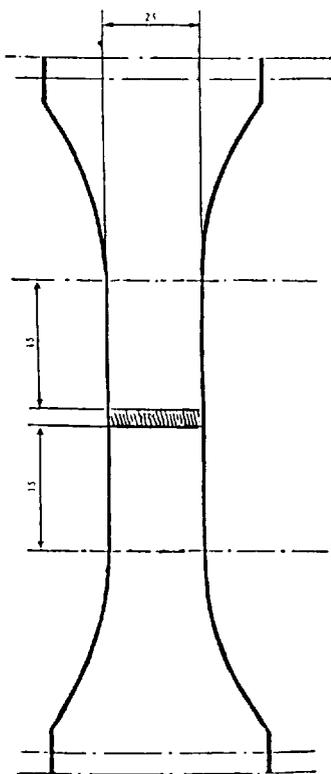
Proveta para ensaio de fracção perpendicular à soldadura (n.º 3.1.2.2.2)
